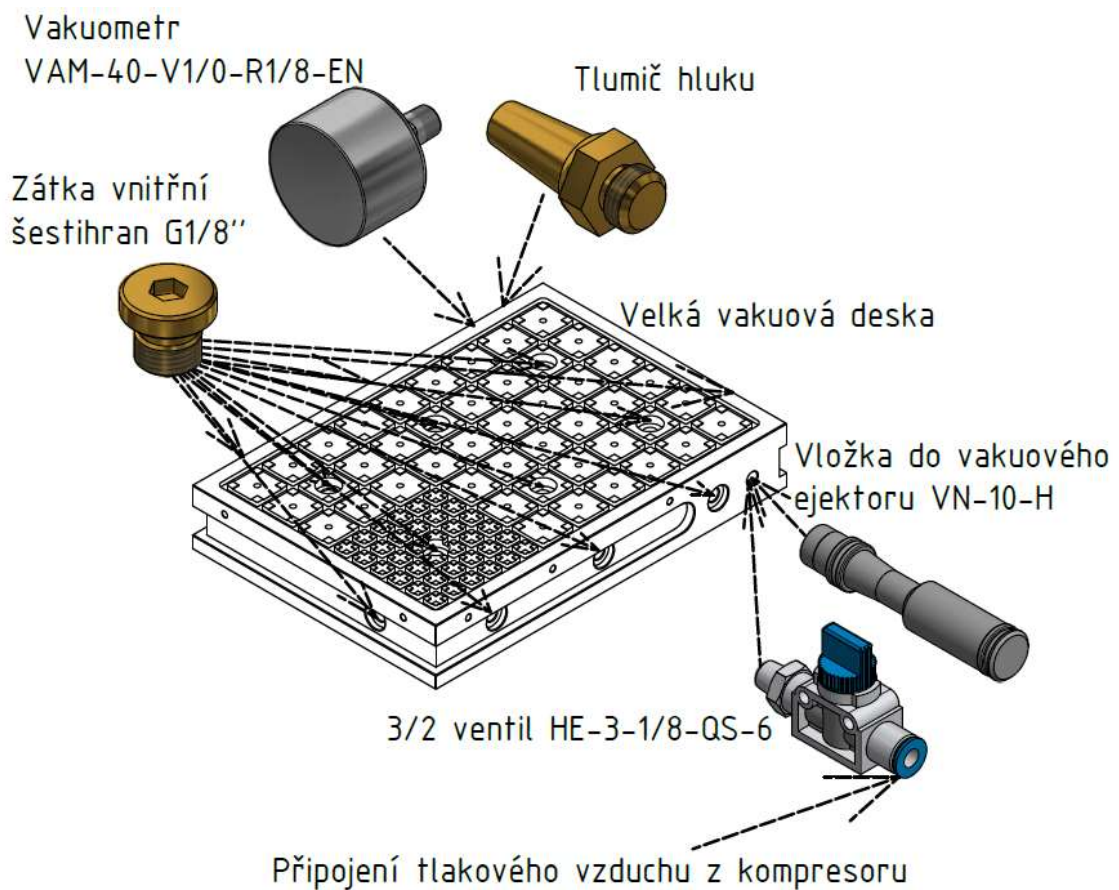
Úplná soustava technologického demonstrátoru
